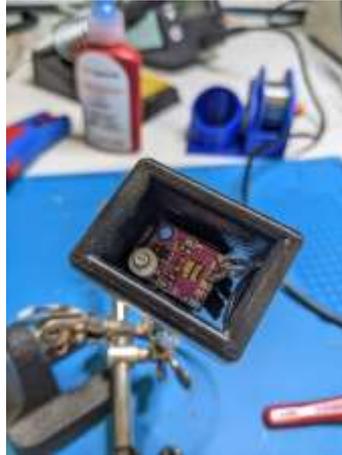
Befestigung des Farbsensors am Gehäuse
